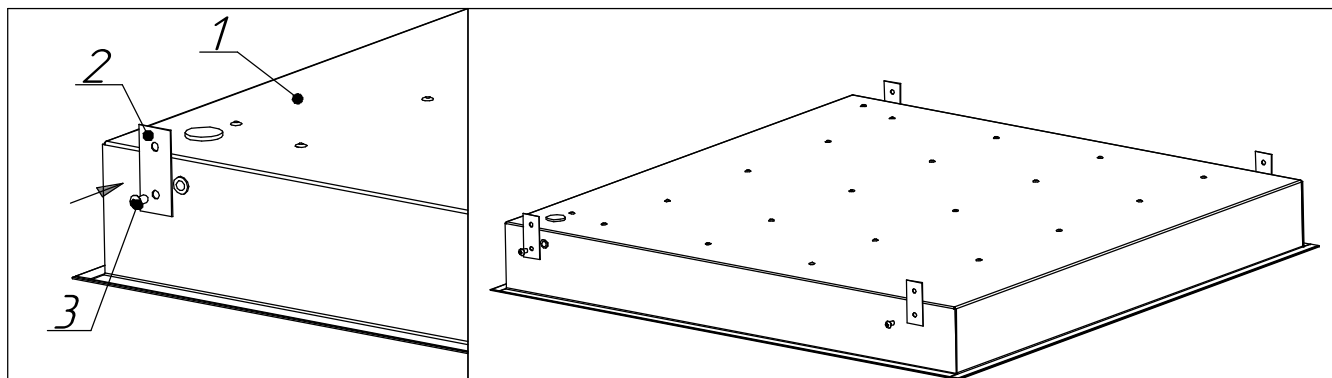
Схема установки пластин для подвеса светильников
